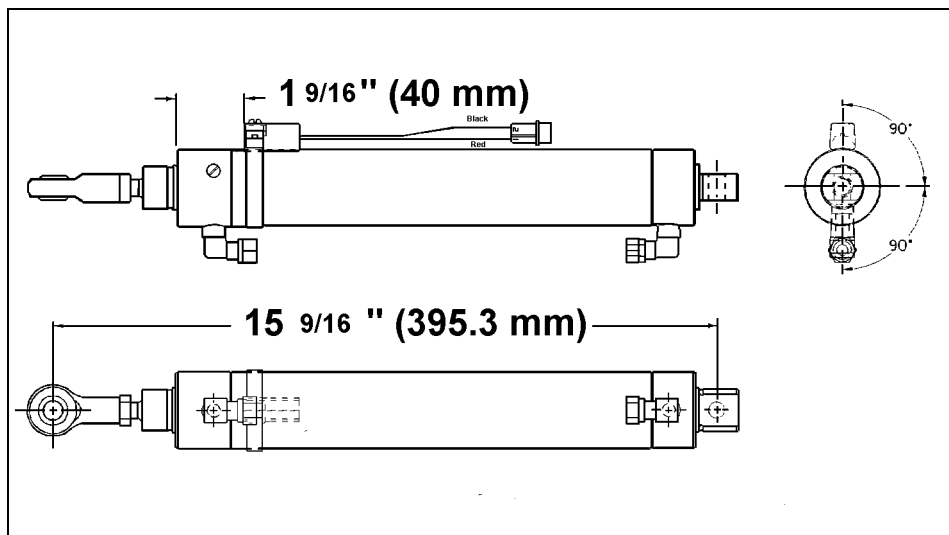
CYLINDRE - ENSEMBLE INTERRUPTEUR
